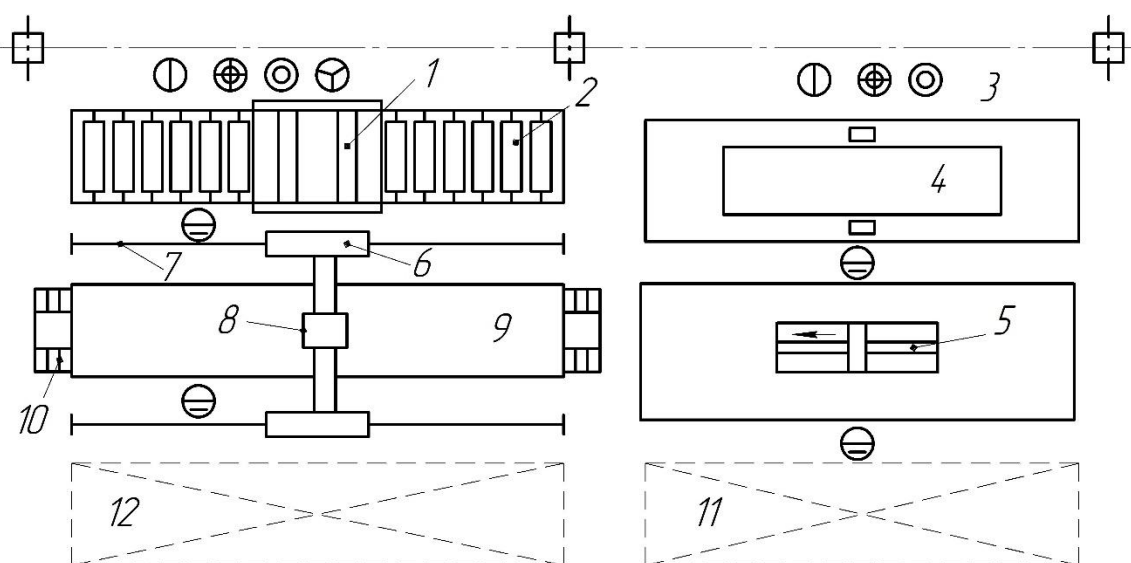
Планировка заготовительного, формовочного и сборочно-сварочного участка поточной линии изготовления труб большого диаметра:
